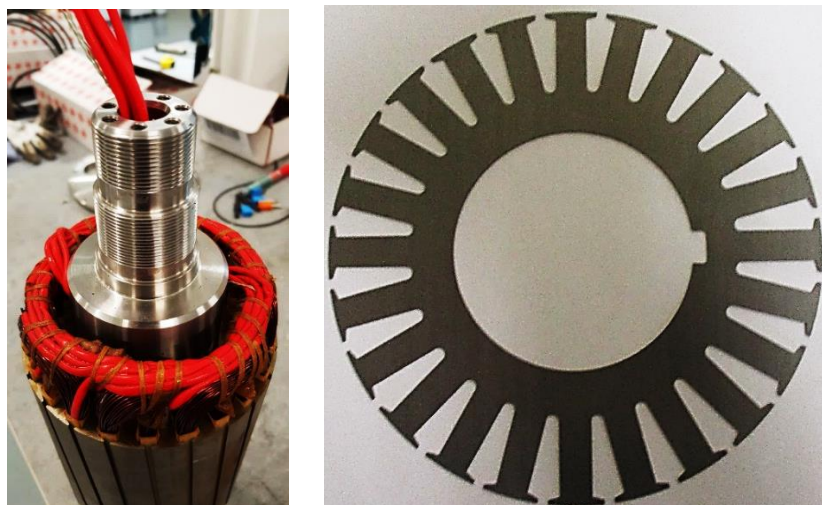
Assemblage stator-arbre ; tôle du stator.
